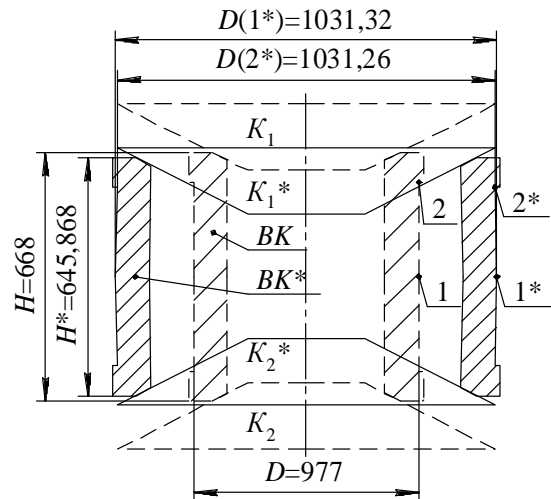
Состояние заготовки в начале и конце процесса гидрорастяжения: D – внешний диаметр кольцевой заготовки; H – высота заготовки; K_1 и K_2 – верхний и нижний конусы соответственно; BK – заготовка; 1 и 2 – точка в центре и на краю цилиндрической поверхности соответственно; обозначения, содержащие «*», обозначают параметр после гидрорастяжения; штриховая линия обозначает начальное положение заготовки и инструмента
